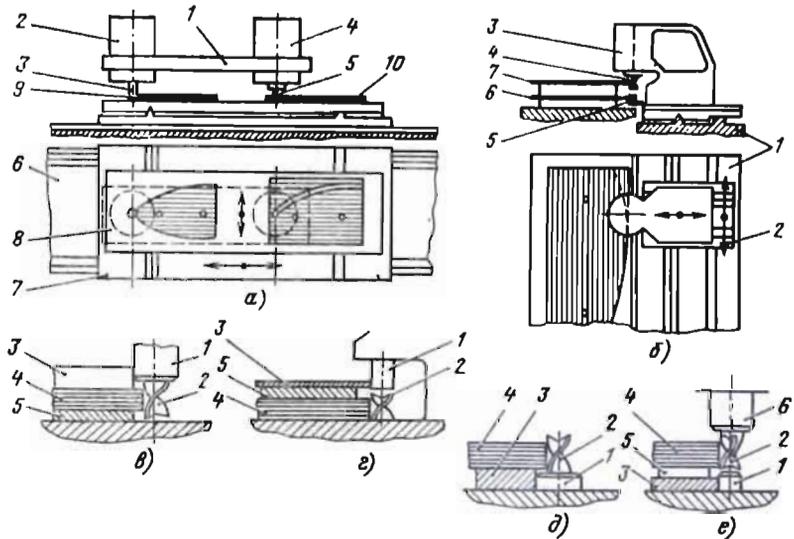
Схемы различных способов копирования при фрезеровании пакета листовых заготовок:
